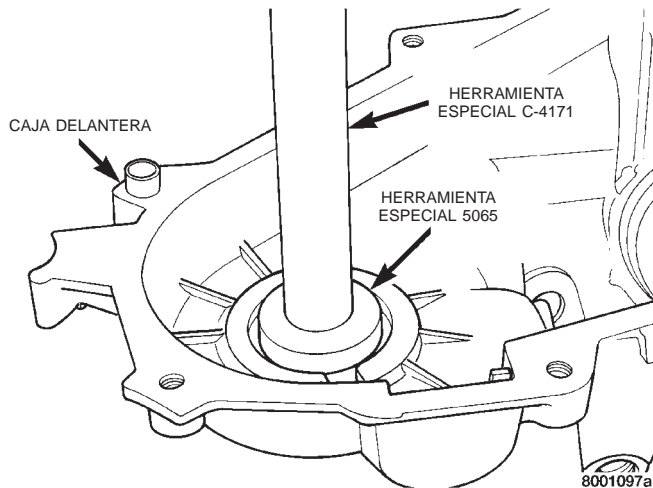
Desmontaje del cojinete del eje transmisor delantero
